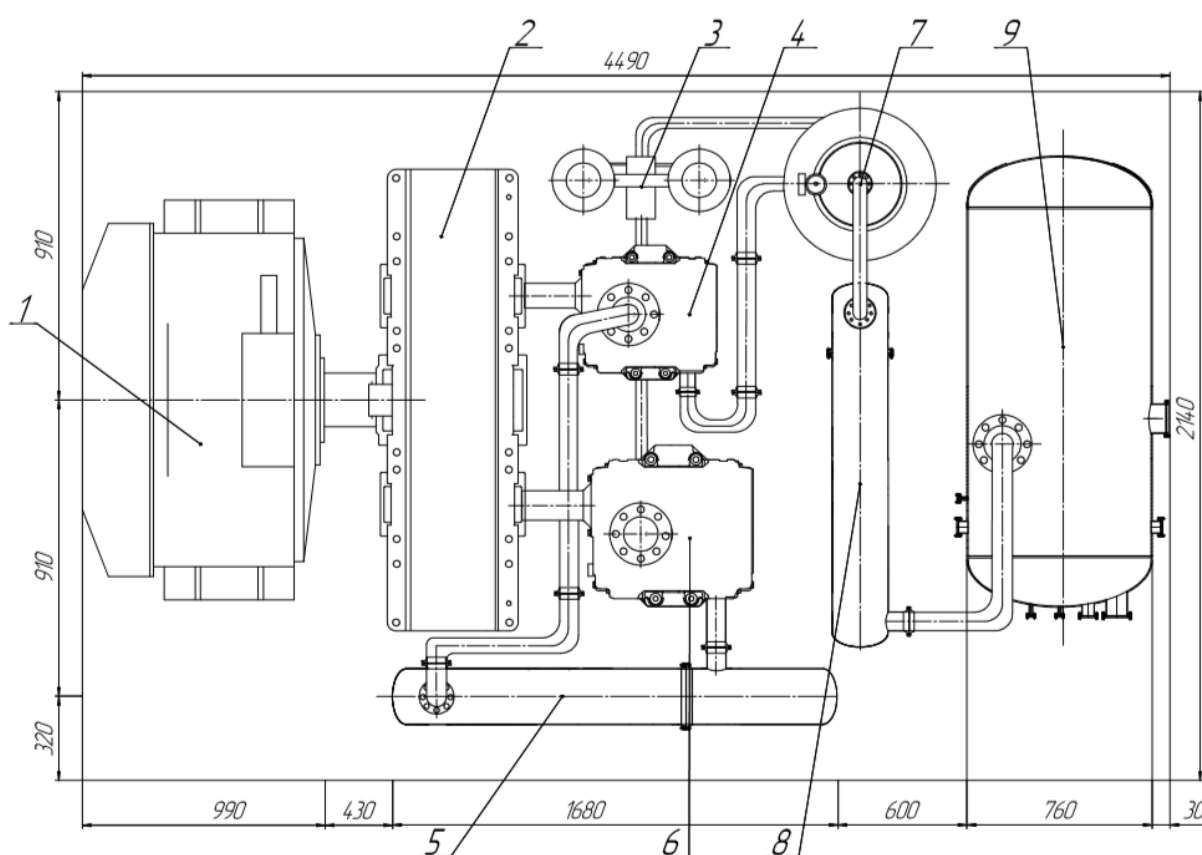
Компоновочная схема передвижной винтовой компрессорной установки
